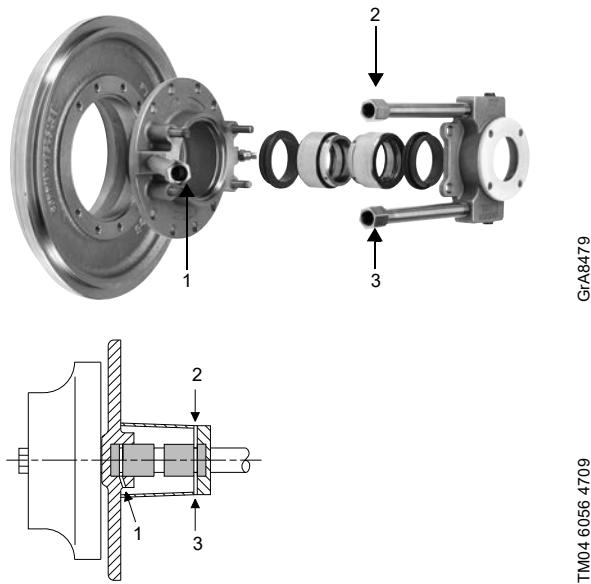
Соединения для подачи затворной жидкости в уплотнении "back-to-back"
